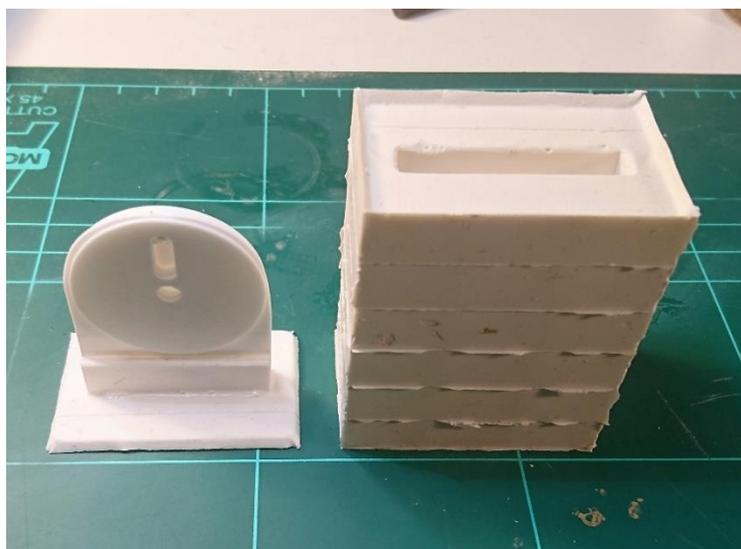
Pieza extraída del molde. Fuente: Trabajo de campo.
